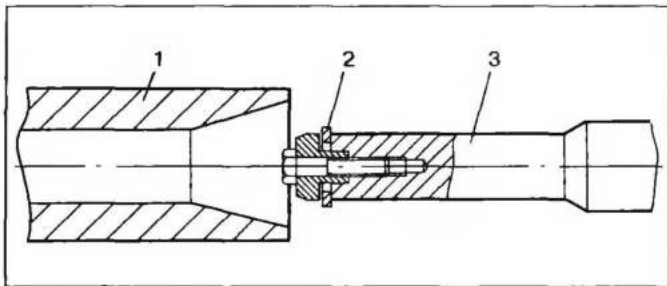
Приспособление для притирки уплотнительного кольца: 1 — гильза; 2 — кольцо; 3 — стержень
